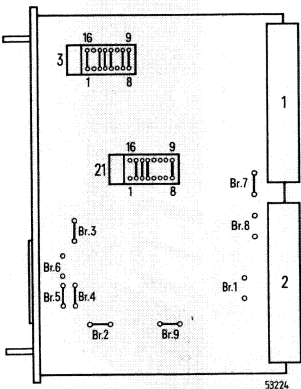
Zentralbaugruppe 6ES5 925-5AA12, Einbaulage der Brücken
